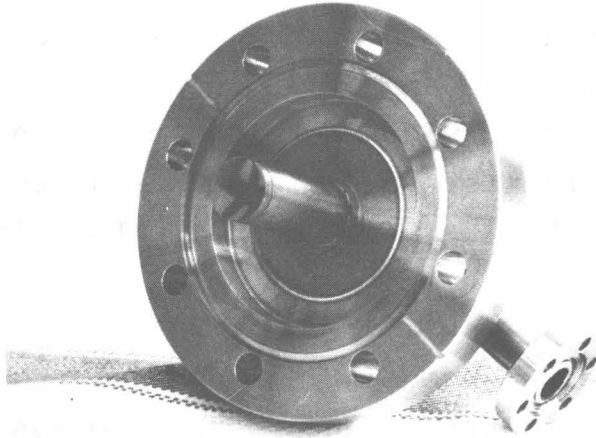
Emitter, in UHV-Flansch eingeschweißt bzw. gelötet
